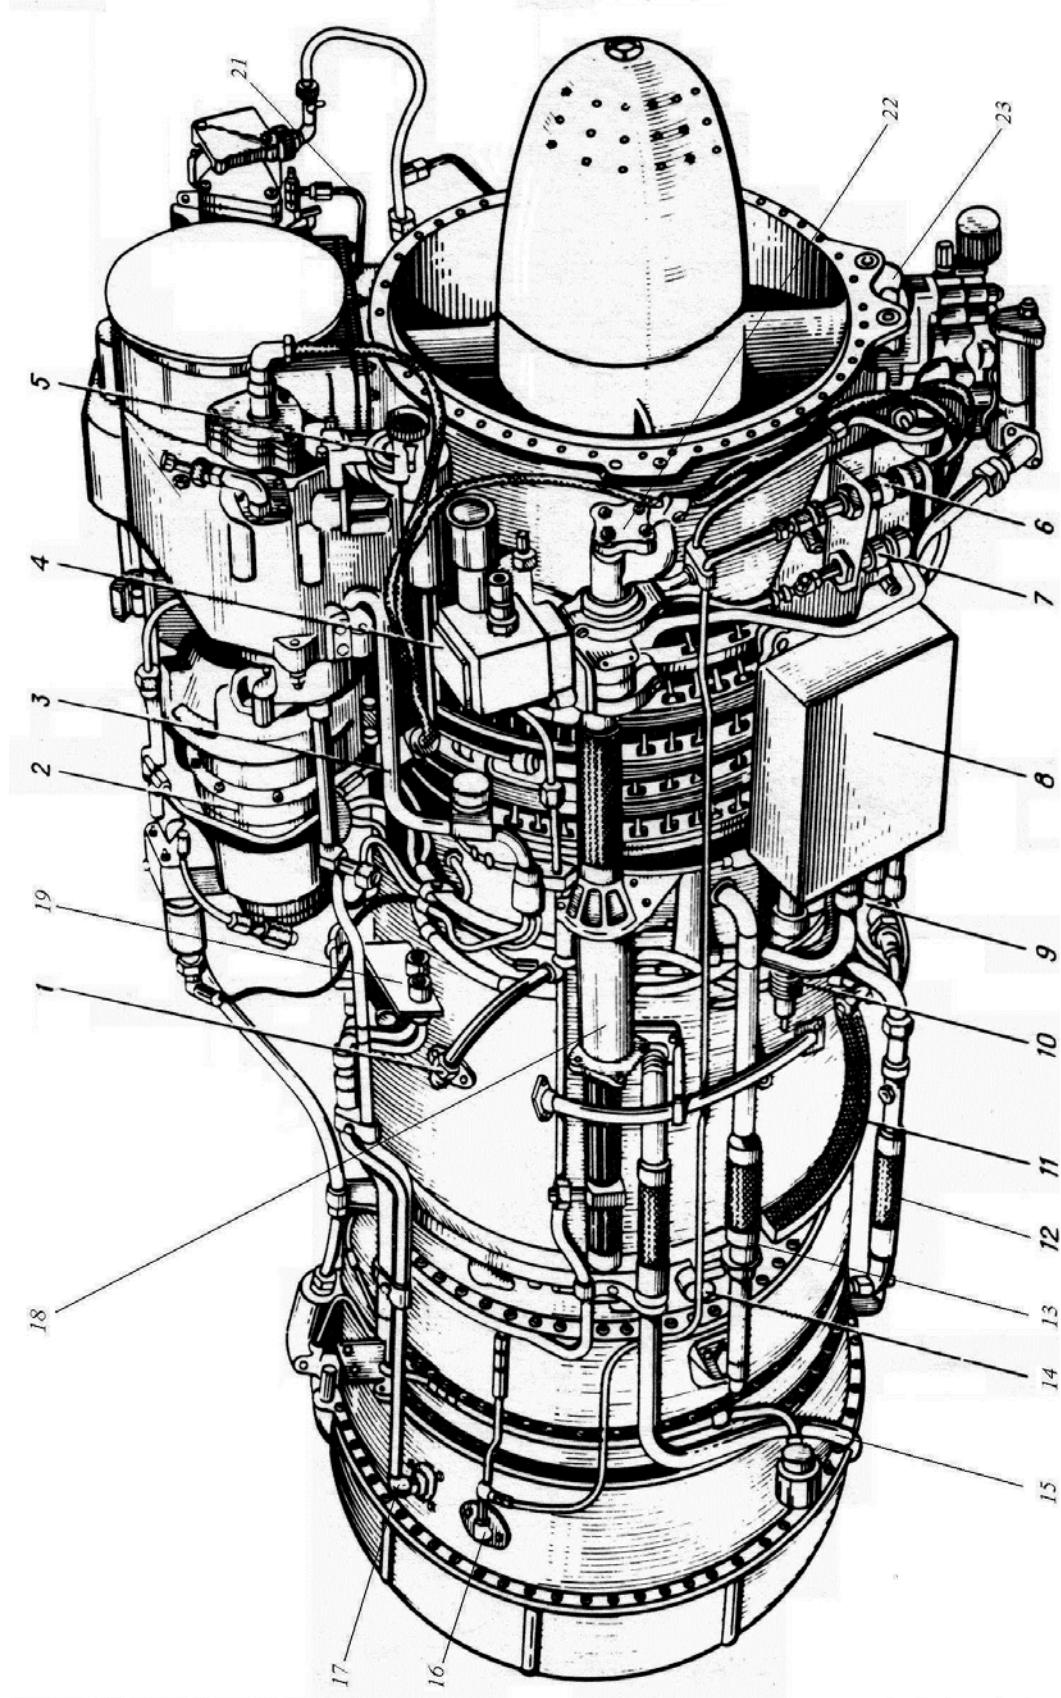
Двигатель ТВЗ-117В (вид слева).
